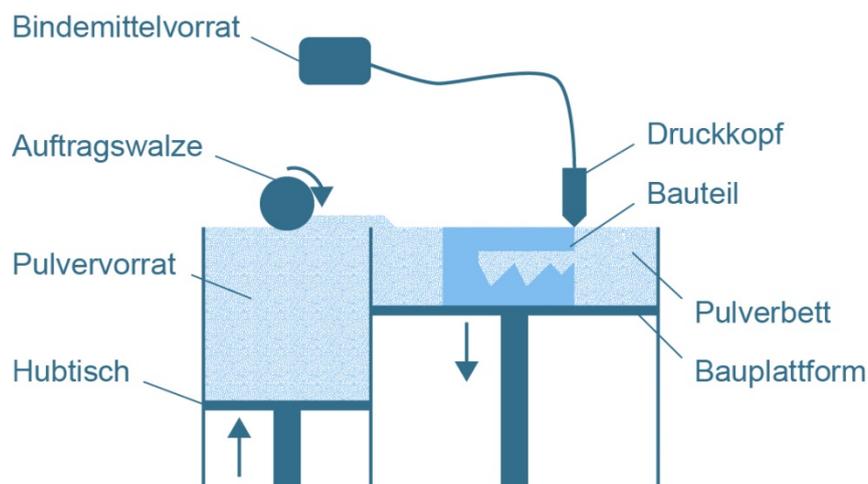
Aufbau und Elemente einer 3-D-Druckanlage
